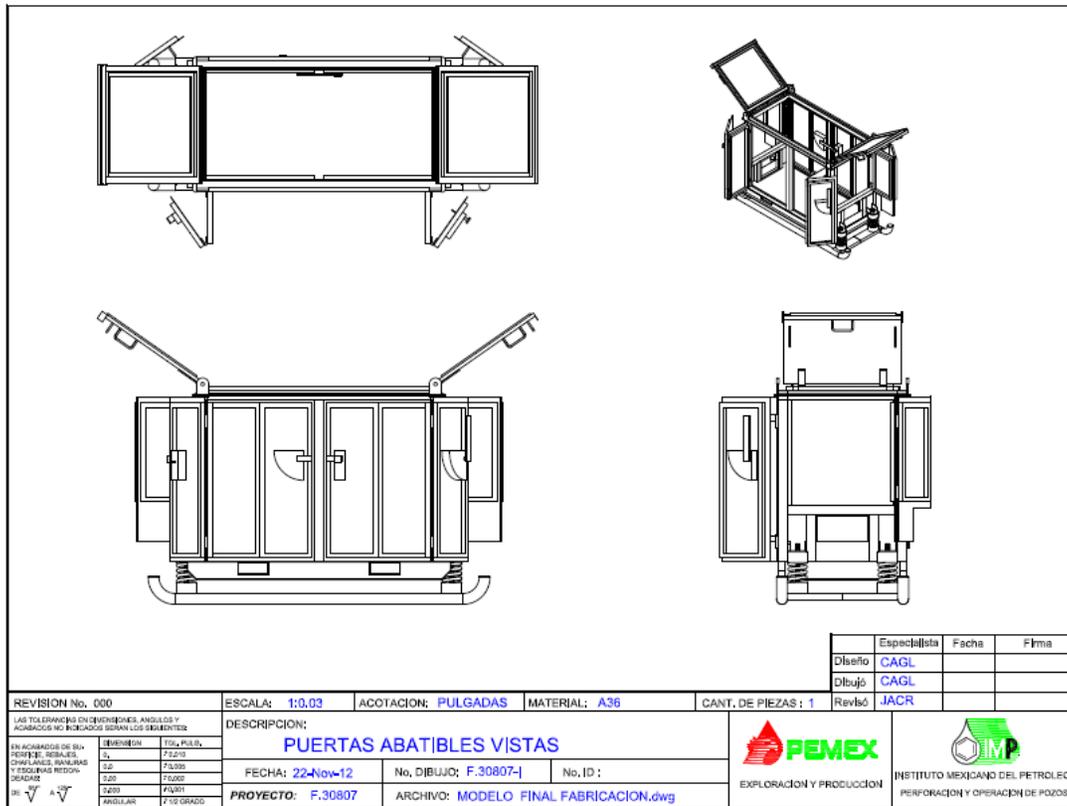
Plano de las vistas del diseño conceptual con sus puertas abatibles.
